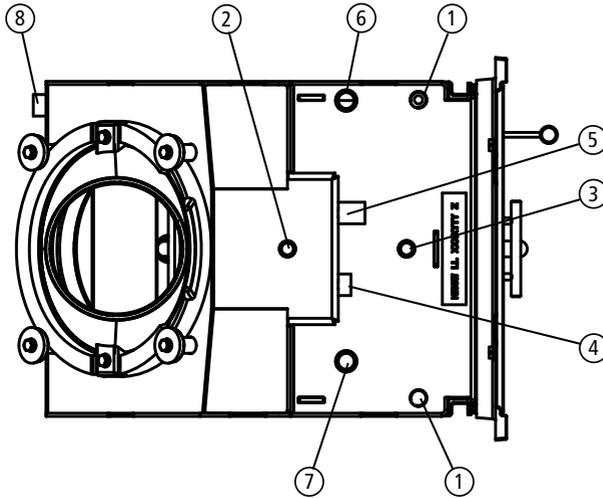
Anschlüsse bei DIAMANT H100 W
